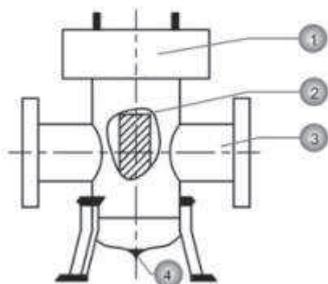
Устройство фильтра для диаметра 50 мм и более. 1 - крышка с болтами крепления; 2 - фильтр-элемент; 3 - корпус; 4 - дренаж
